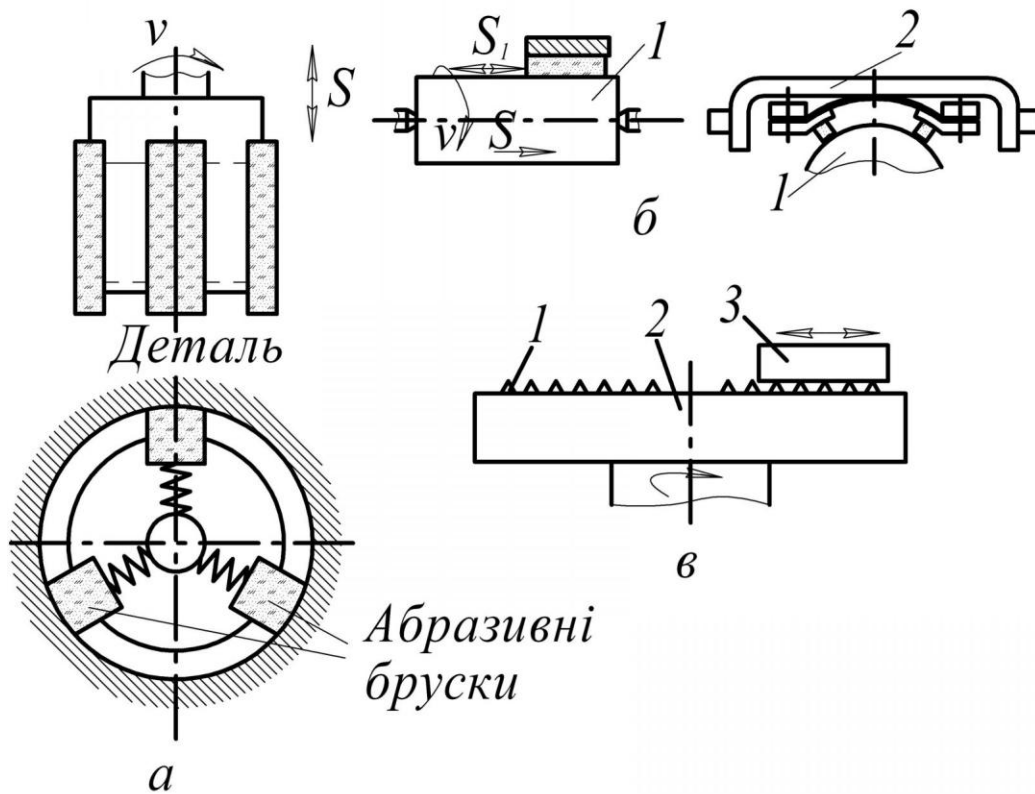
Схеми чистової обробки поверхонь деталей машин
